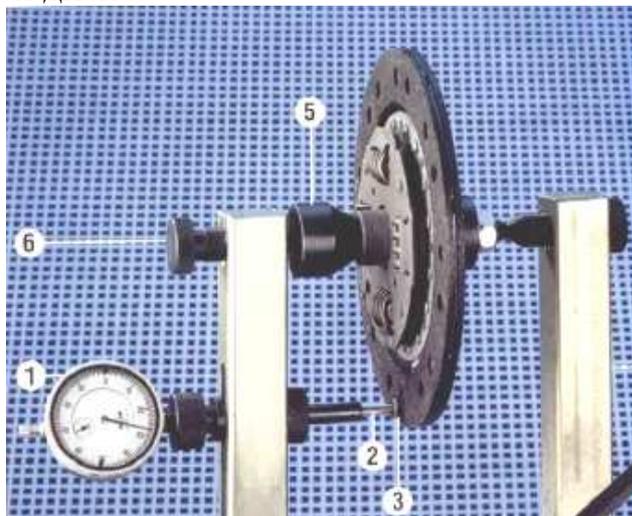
Проверка биения рабочей поверхности ведомого диска.
